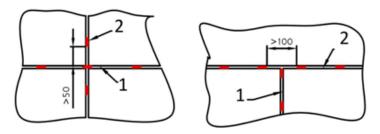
Установление прихваток на пересечении сварных швов в очерёдности (1, 2).
